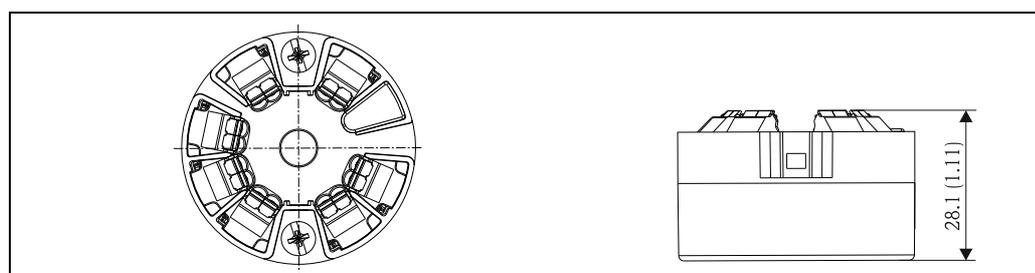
Ausführung mit Federklemmen. Abmessungen sind identisch der Ausführung mit Schraubklemmen, außer Gehäusehöhe.
